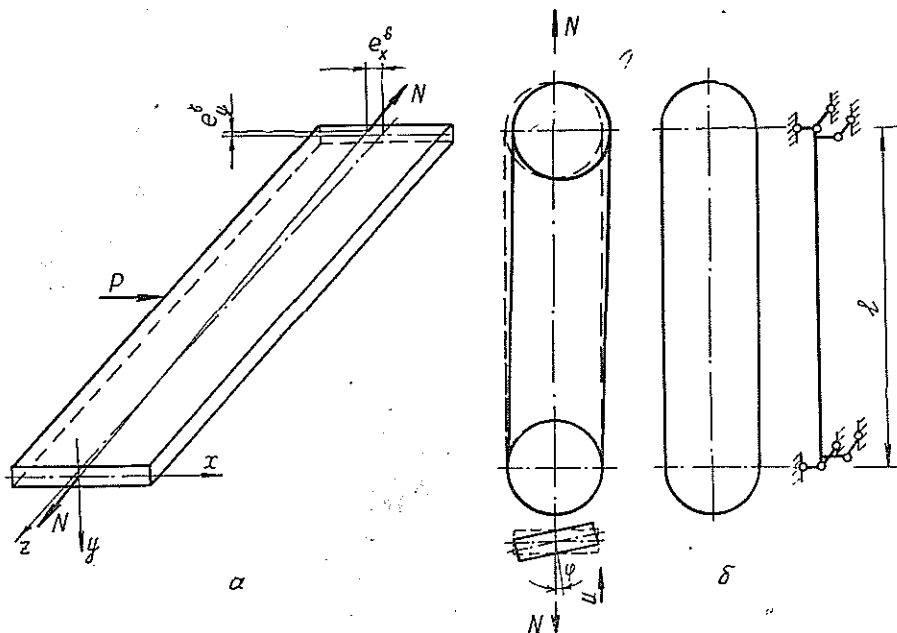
Расчетная схема для исследования влияния разворота верхнего шкива на устойчивость ленточной пилы (а) и схема разворота верхнего пильного шкива (б)
